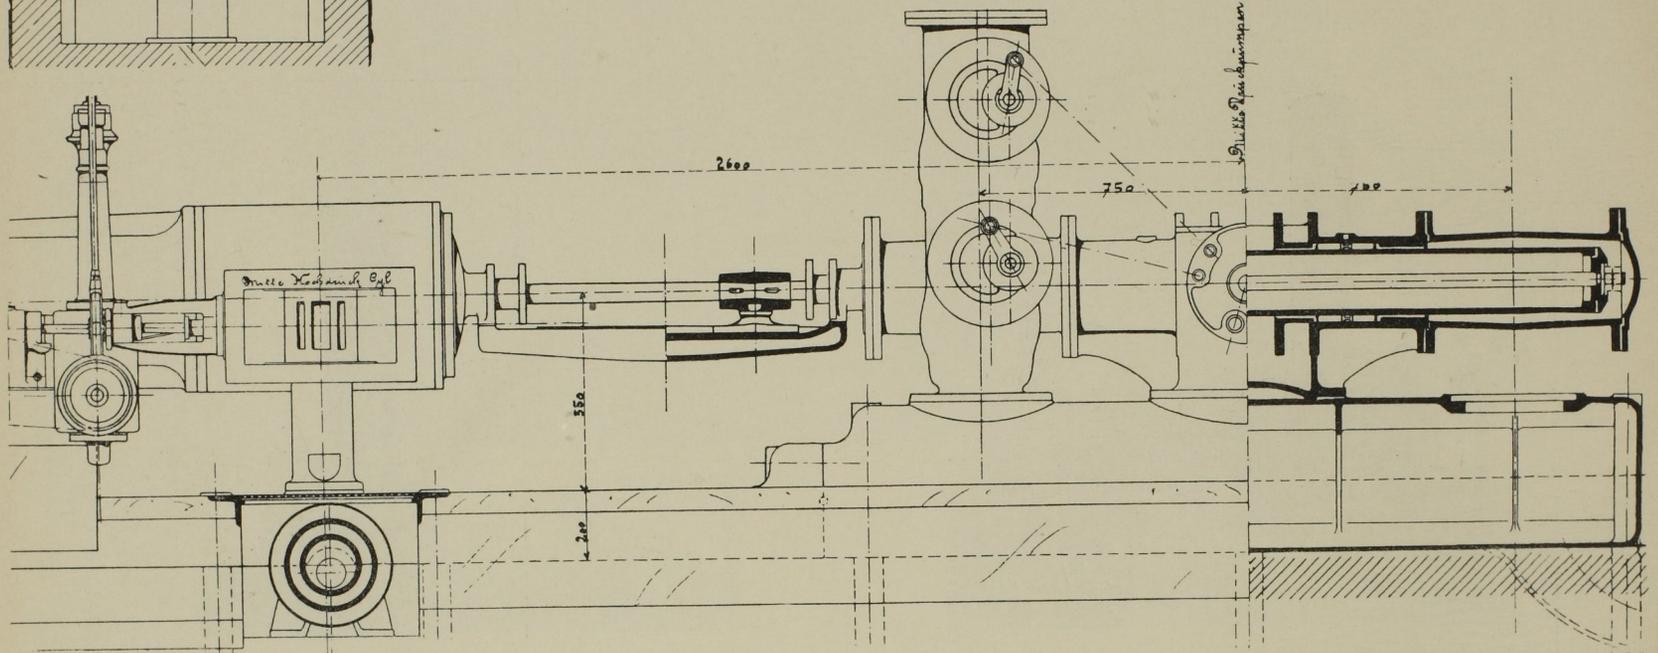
Seitenansicht und Längsschnitt der Druckpumpmaschine. Masst. 1:20.
